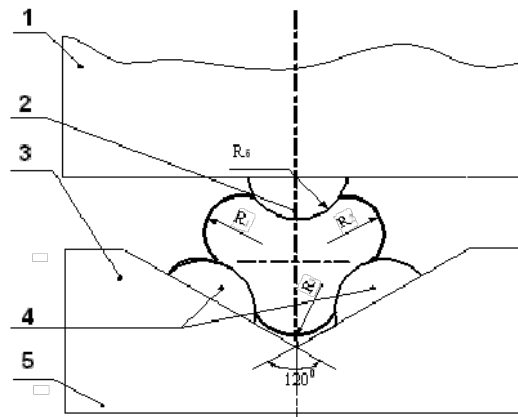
Обжатие заготовки комбинированными профилированными бойками
